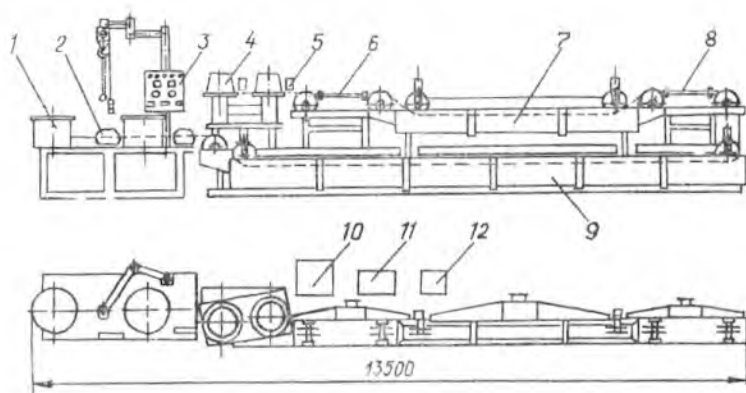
Общий вид установки ОБ 2175 для электрохимической очистки сварочной проволоки
